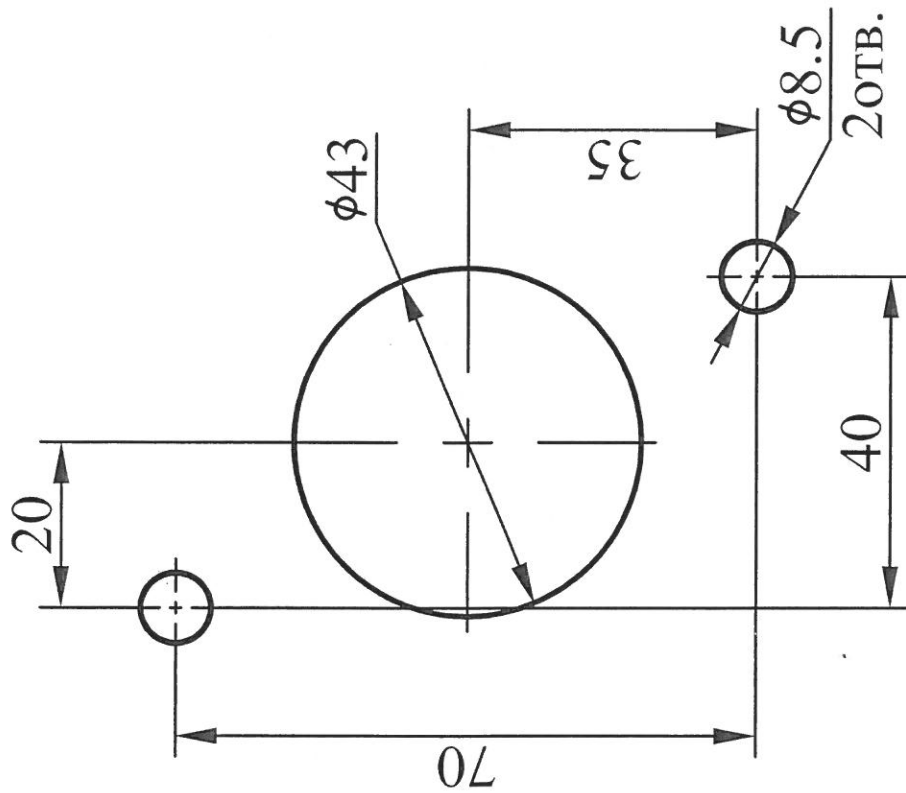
Разметка отверстий для установки привода ГРК-10Б (вид спереди)
